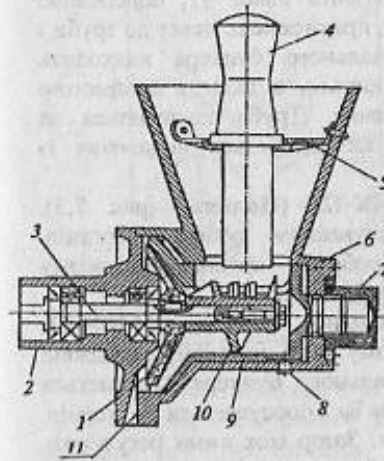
Механізм для подрібнення сухарів та спецій МИ: 1 – тертковий диск; 2 – хвостовик; 3 – вал; 4 – штовхач; 5 – решітка запобіжна; 6 – корпус; 7 – гайка; 8 – гвинт; 9 – тертковий барабан; 10 – шнек; 11 – розвантажувальний пристрій
